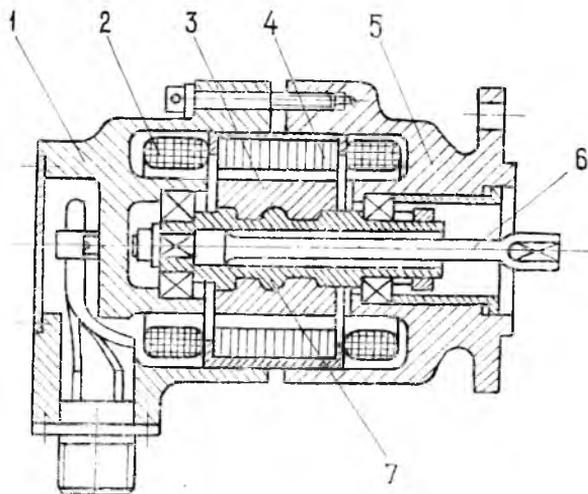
Датчик тахометра типа ИТЭ: 1—крышка корпуса; 2—обмотка статора; 3—ротор-магнит; 4—статор; 5—крышка корпуса с фланцем крепления; 6—рессора; 7—втулка
